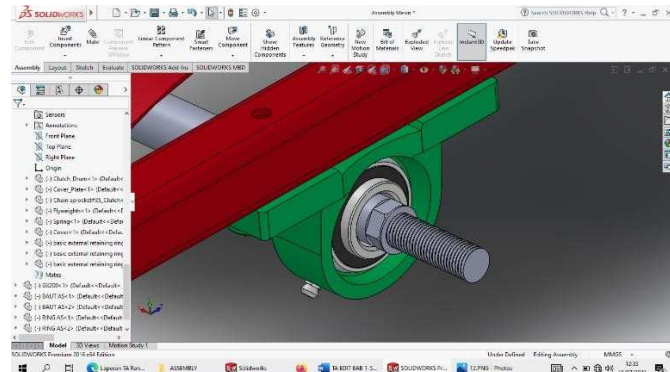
152 Hasil *Assembly Bolt* dan Poros Roda
